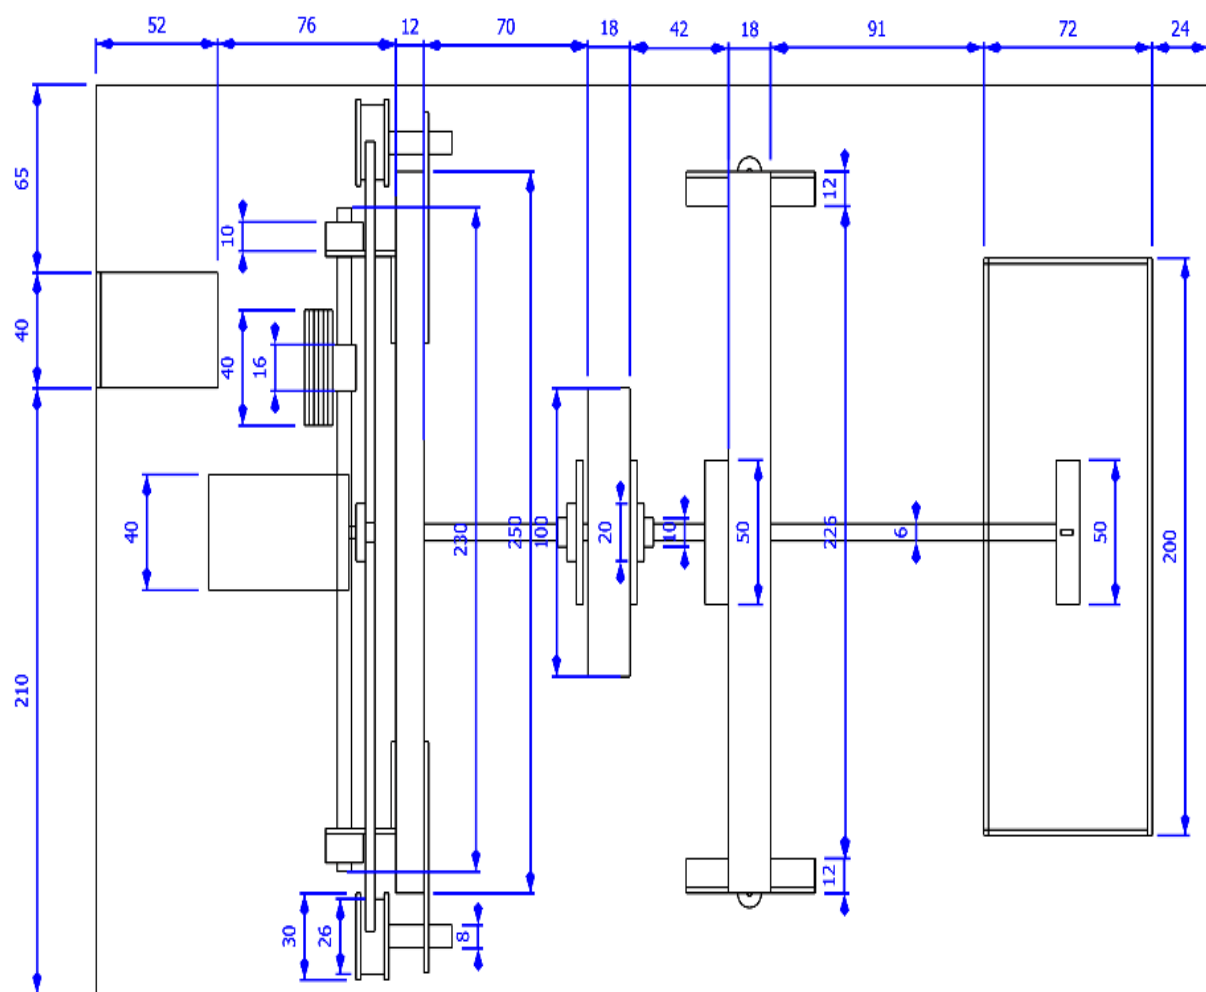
Esquemático da Planta de Teste - Vista Superior
